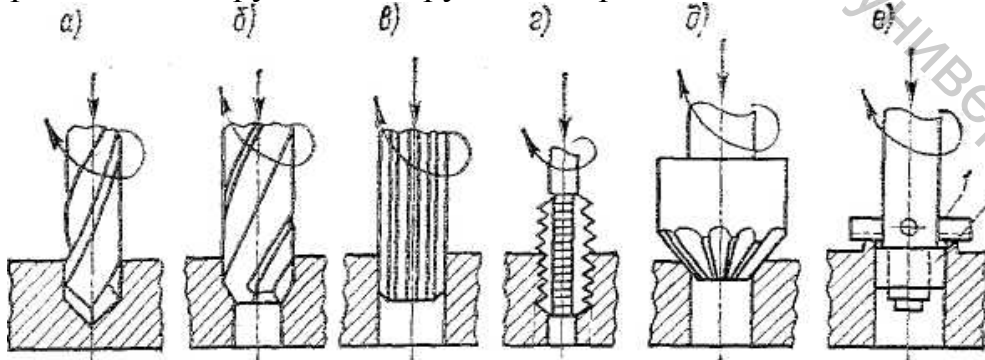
Виды работ, производимых на сверлильных станках: а- сверление; б- зенкерование; в- развертывание; г- нарезание резьбы; д- зенкование; е- цекование.
